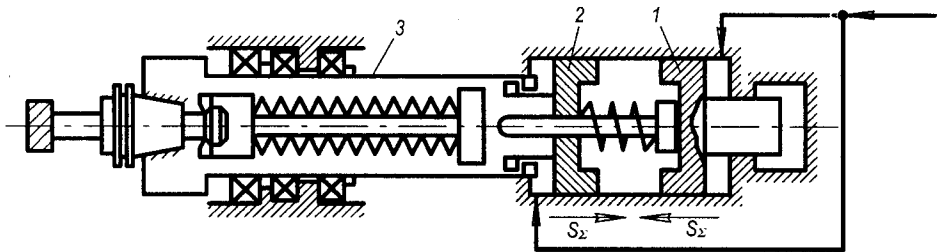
Механізм автоматичного затискання інструмента з поршневим гідромеханічним приводом і розвантаженням опор шпинделя
